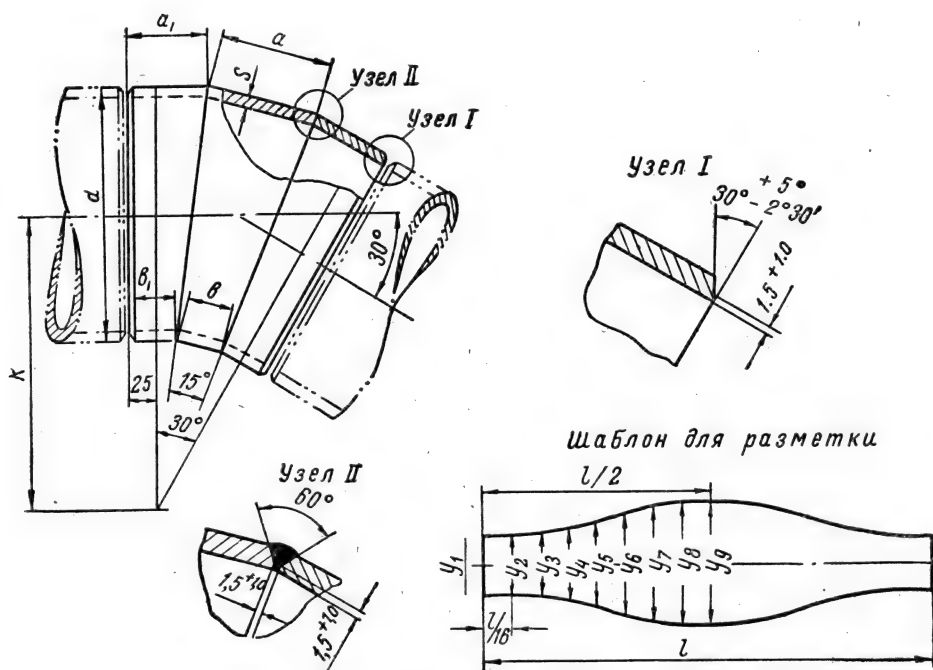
Отвод сварной с углом поворота 30° .
